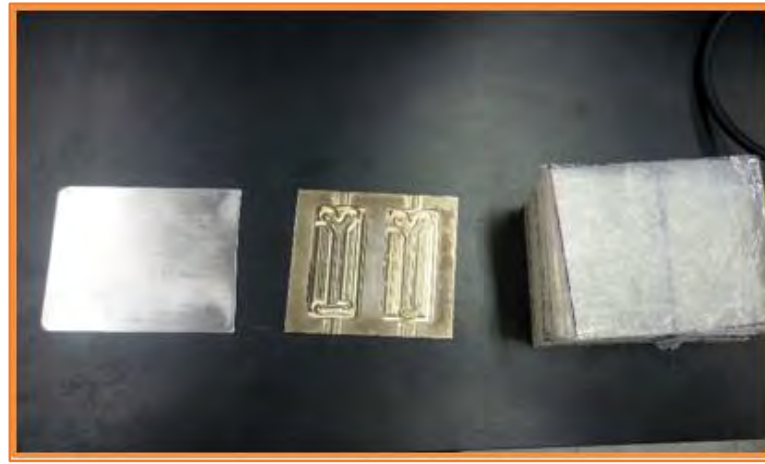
Fotografía de la placa de acero, molde de la microcelda de combustible y placas de PMMA.
